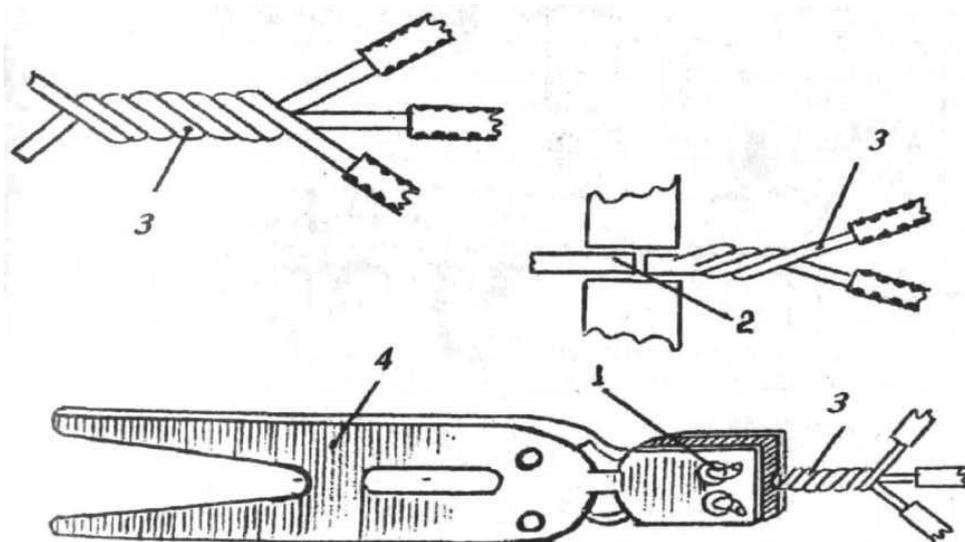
Клещи КСП (процесс опрессовки): 1 - губки клещей; 2 - опрессованная скрутка жил; 3 - скрутка из очищенных жил; 4 - ручки клещей.
